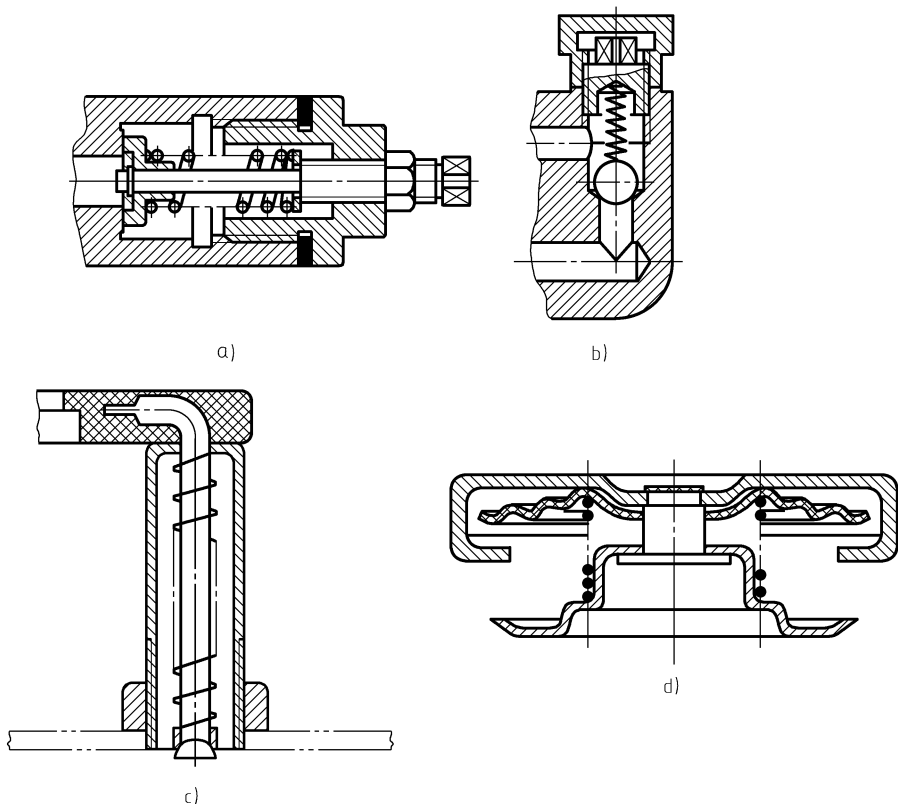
装配图中圆柱螺旋压缩弹簧的画法
